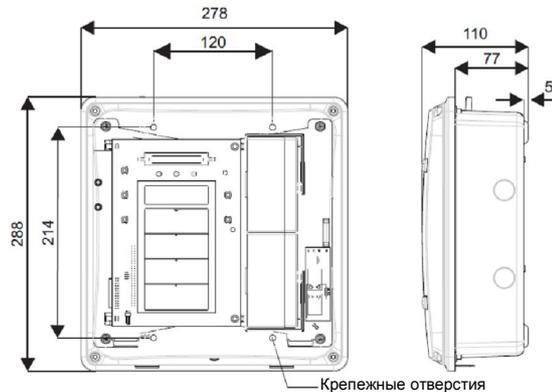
Габаритный чертеж панели Gasmaster (показаны крепежные отверстия)
